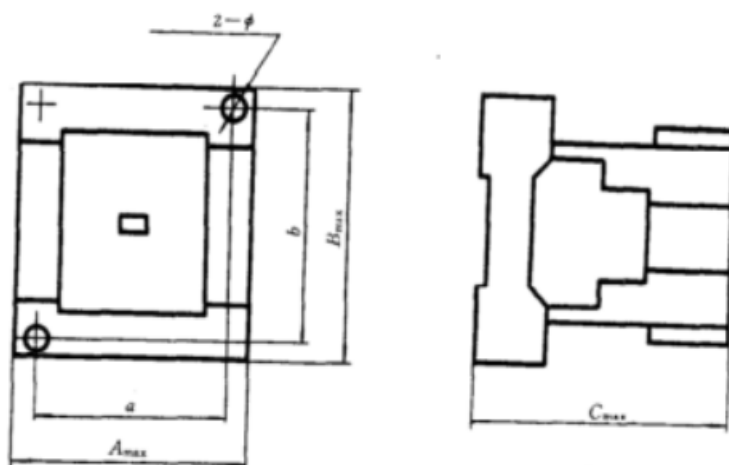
CJX 1-32~170、CJX 3-32~170 型交流接触器外形尺寸与安装尺寸
